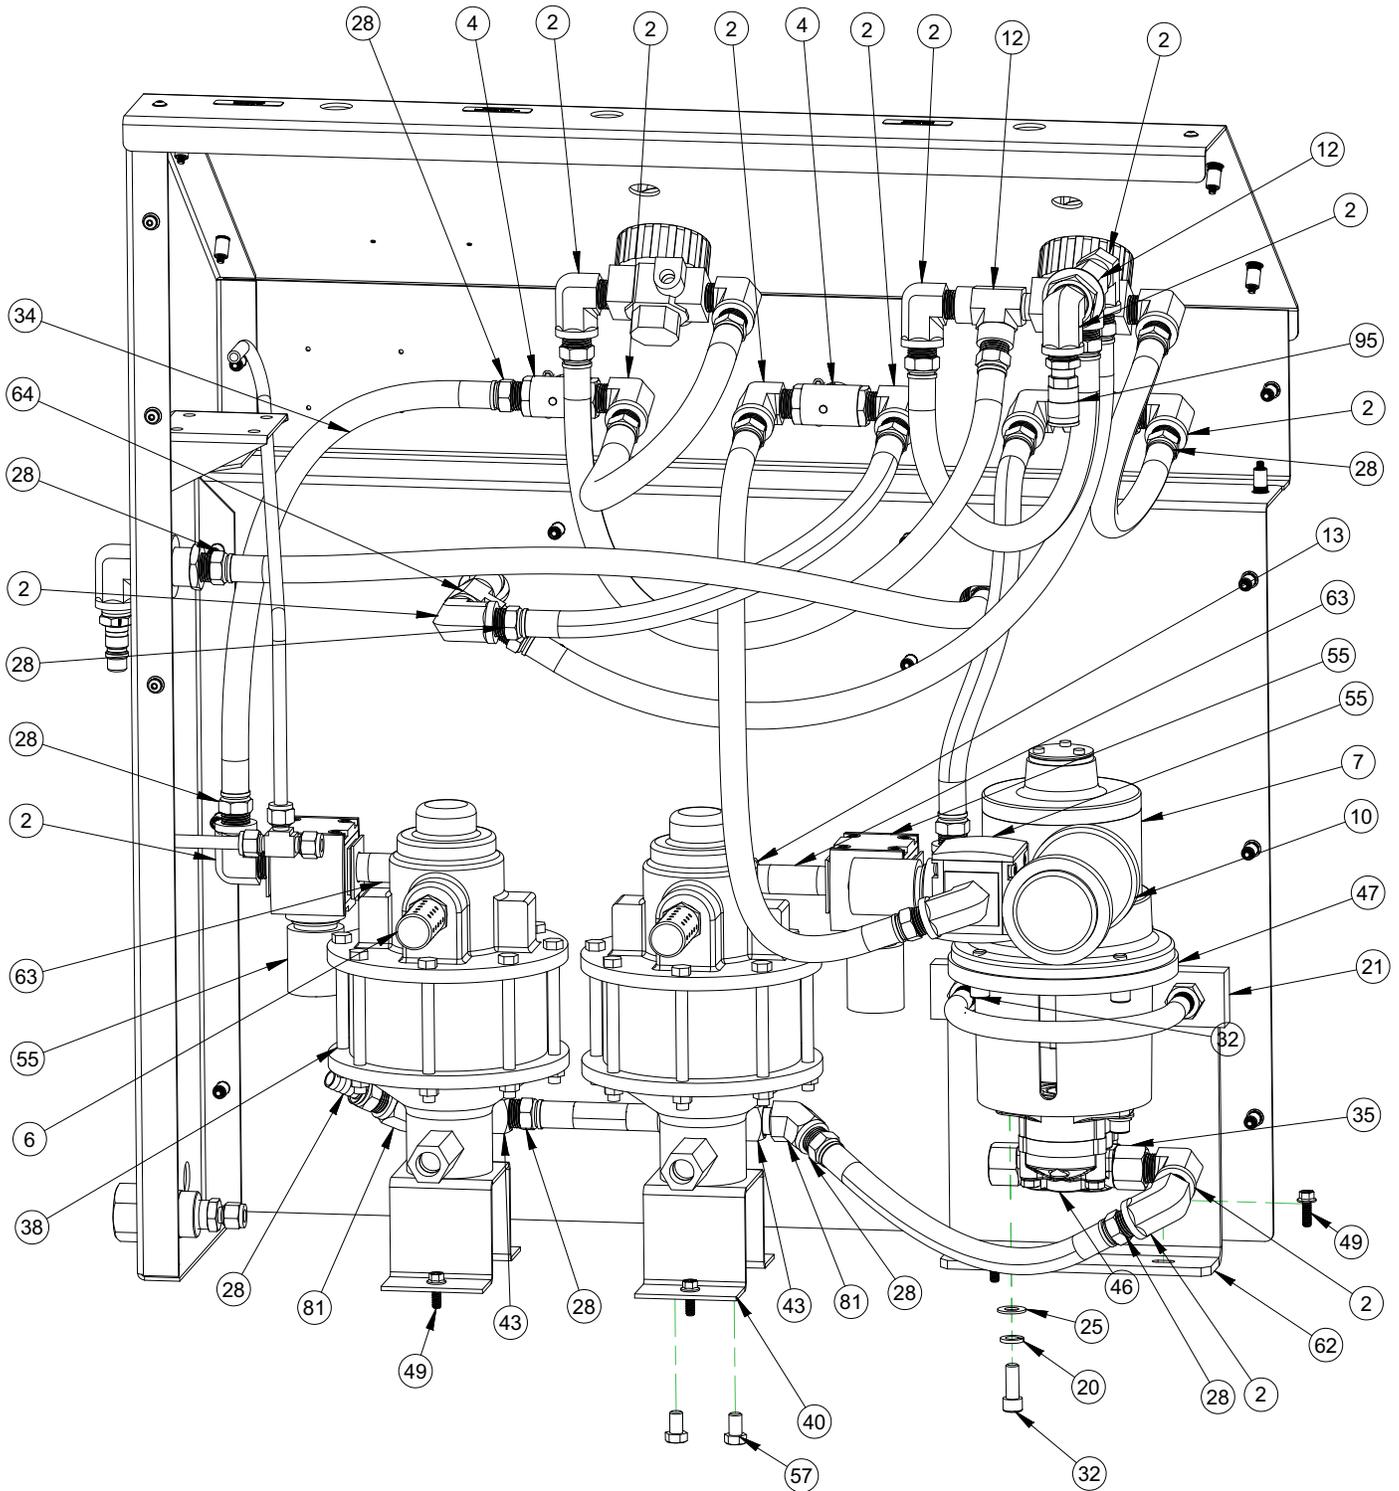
ENSAMBLAJE DETALLADO DE LA CONSOLA (P/N 88479)
